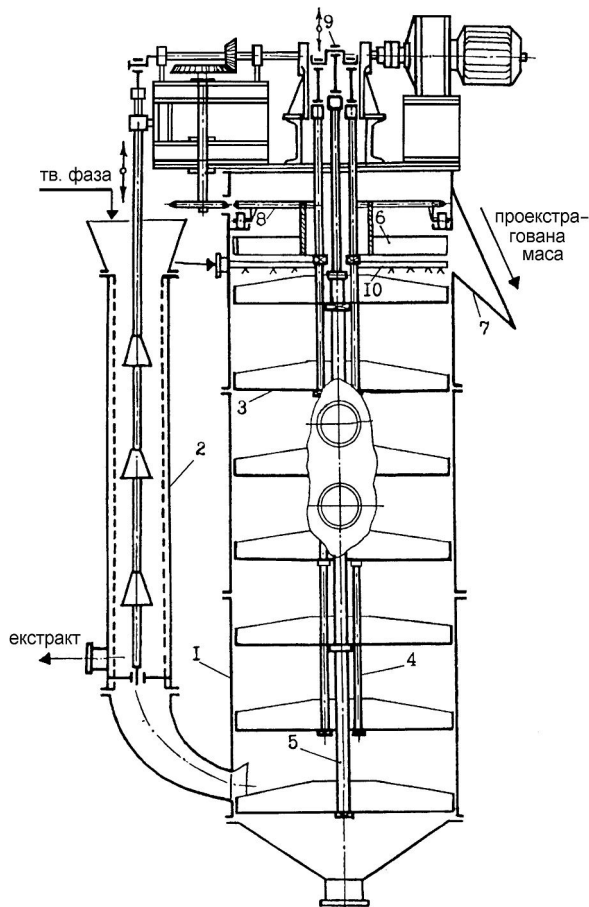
Принципова схема віброекстрактора: 1 – корпус апарата; 2 – завантажувальний пристрій; 3 – вібротранспортувальна тарілка; 4, 5 – штоки; 6 – шкребачка; 7 – лоток; 8 – механізм для розвантаження; 9 – вібропривід; 10 – зрошувач
